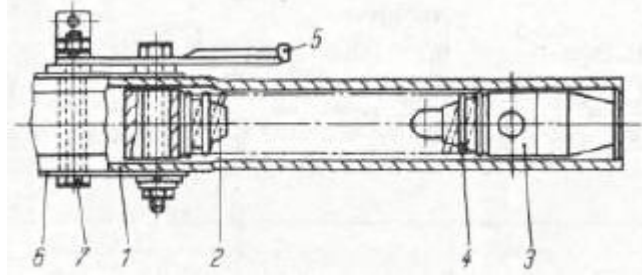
Kupplungsrohr 1 mit Gummitteil vorn 2, Gummitteil hinten 3, Druckfeder (C 3,6 x 40 x 17,5 B) 4, Auflaufanschlag 5, Kugelkupplung 6, Sechskantschraube M 12 mit Mutter und Federring 7
